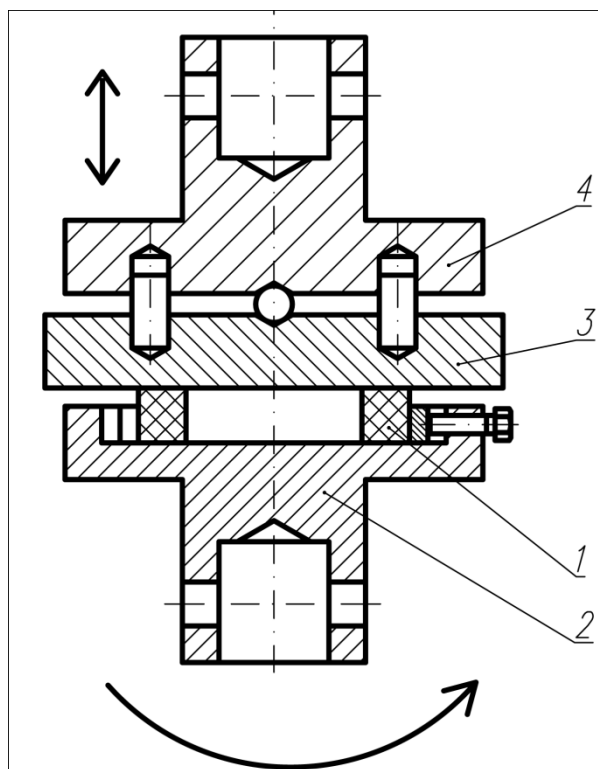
Приспособление для исследования изнашивания: 1 - кольцевой образец; 2 – захват; 3 – контртело; 4 - самоустанавливающийся захват
